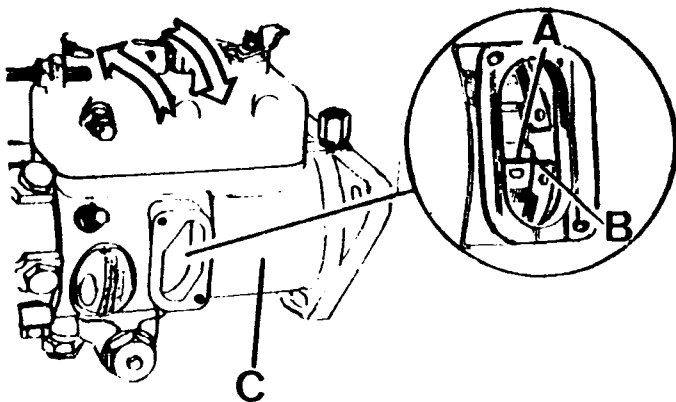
A Ajuste de la bomba una vez -- montada en el motor
